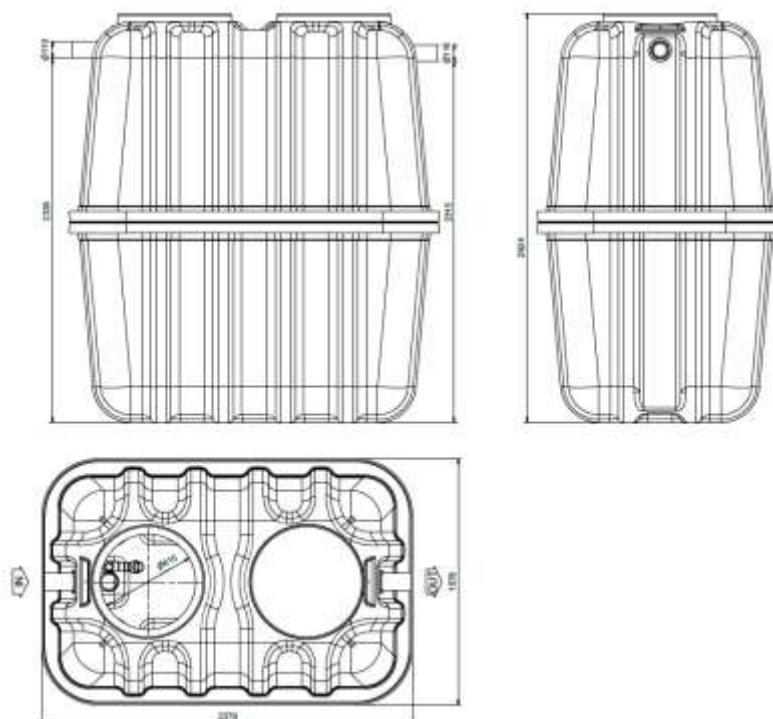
Plan d'encombrement d'une cuve de 7500L
